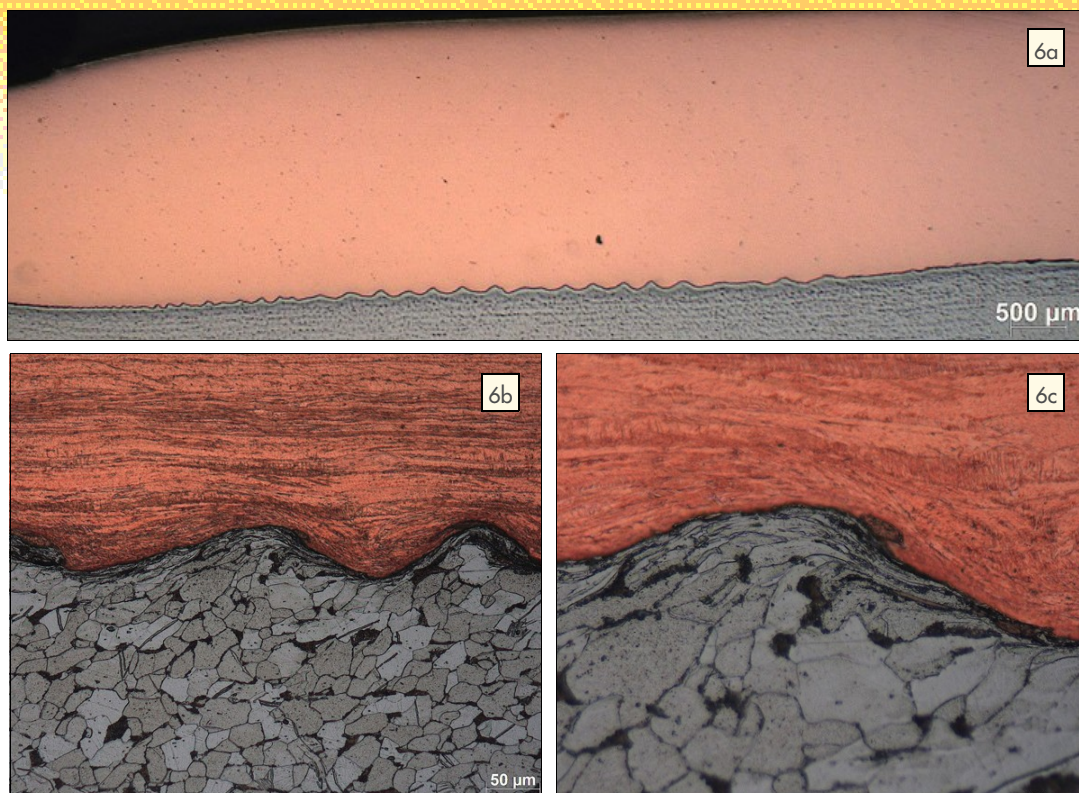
section métallographique d'une soudure cuivre/acier typique (x12)
